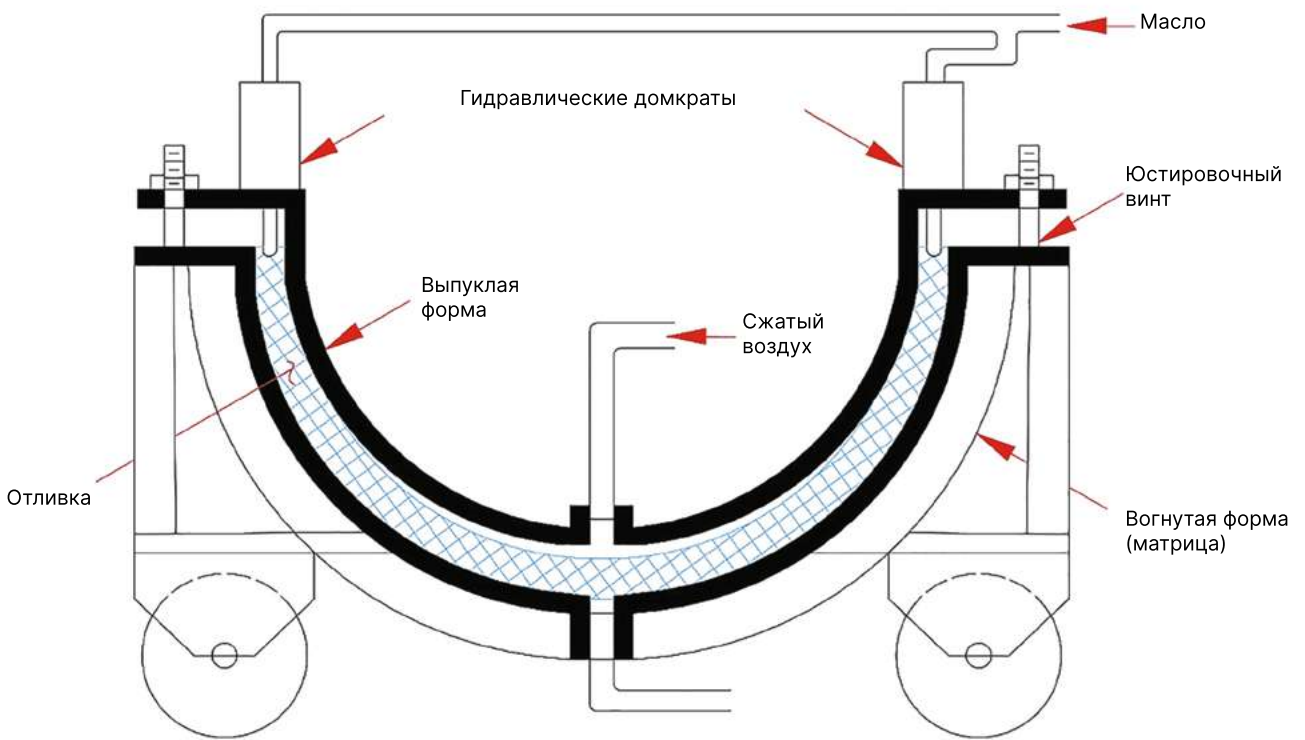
Разделение выпуклой пресс-формы от материала литья акриловой заготовки
